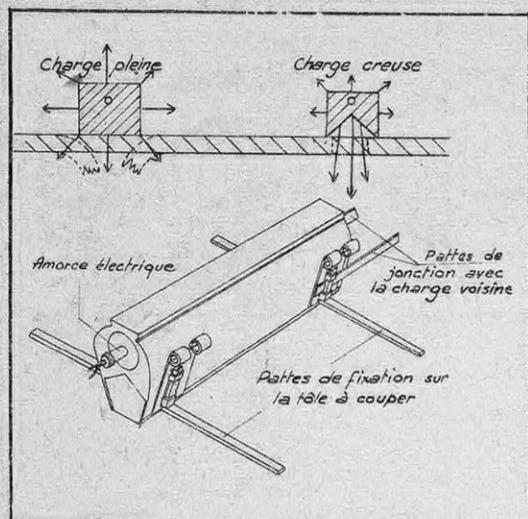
DÉCOUPEUR PYROTECHNIQUE A CHARGE CREUSE
